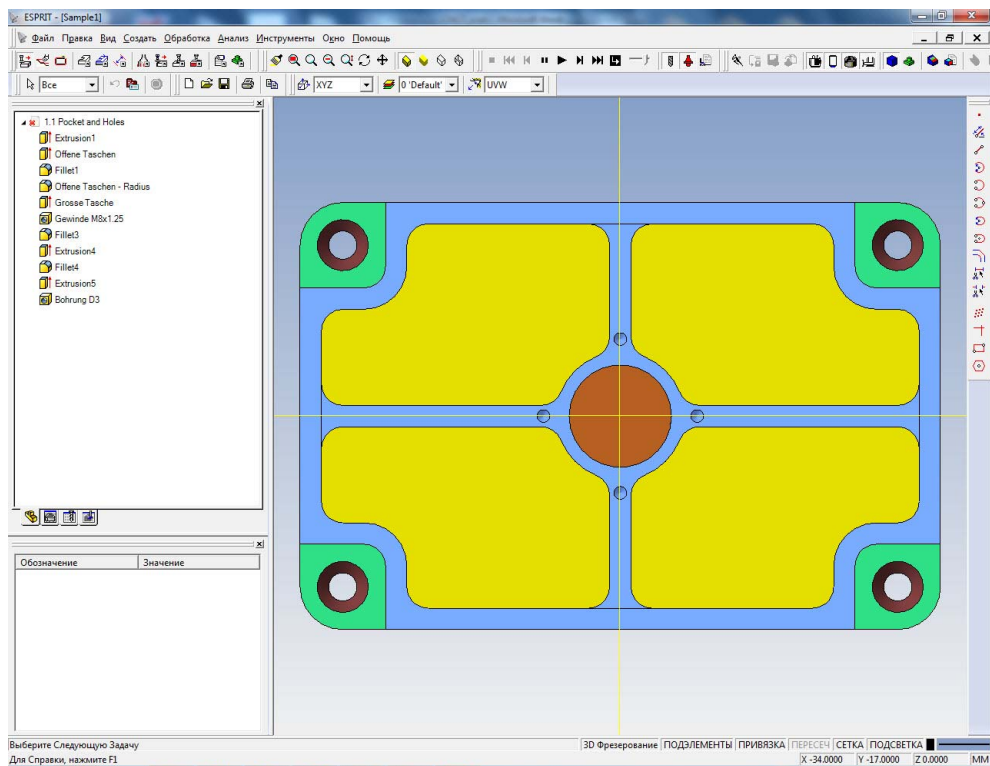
3D-модель корпусной детали для фрезерной обработки
